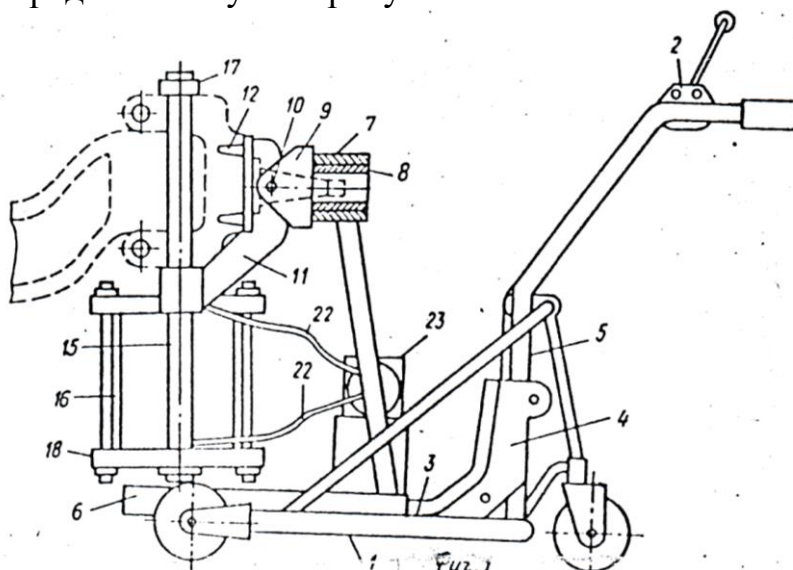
Устройство для выпрессовки шкворней поворотных цапф
